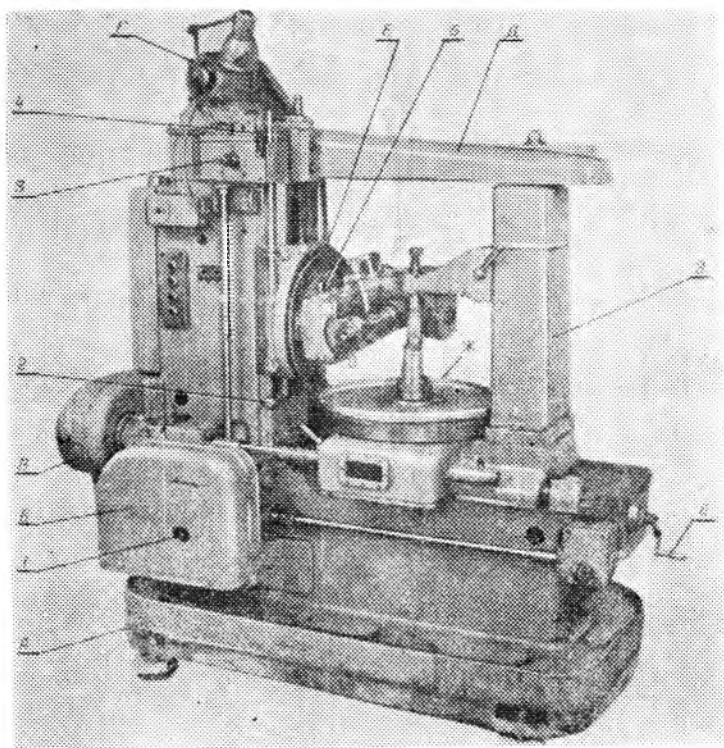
Основные узлы и органы управления зубофрезерным станком 532:
